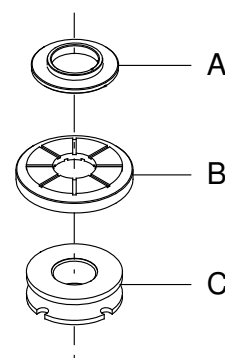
Bague d'arrêt (parties mobile et fixe) et cône de serrage
